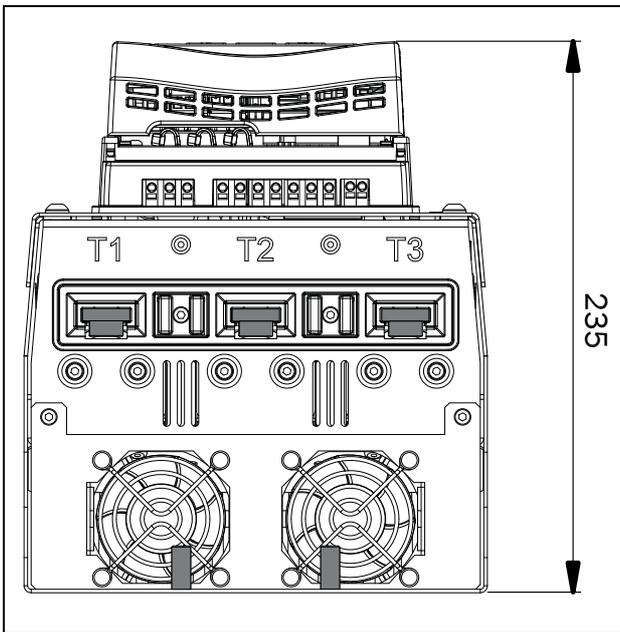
Dimensions du format de châssis 3 du TSA, vue du dessous
